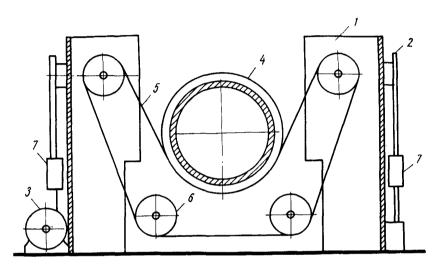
Схема ременной центрифуги I - станина; 2 - ограждение; 3 - электродвигатель; 4 - форма; 5 - несущие ремни; 6 - шкив; 7 - домкрат.
